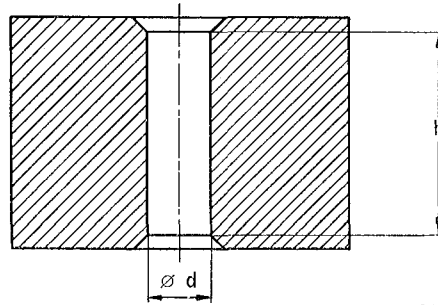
Socle d'essai pour cartouches 6,3 mm × 32 mm.
